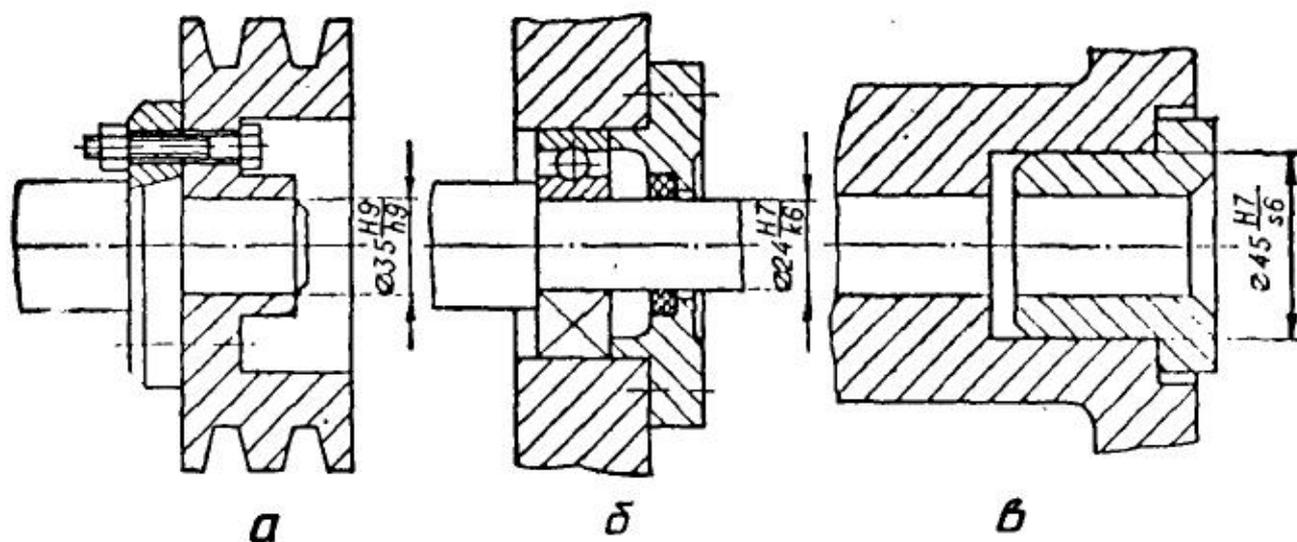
З'єднання деталей по циліндричних поверхнях.
